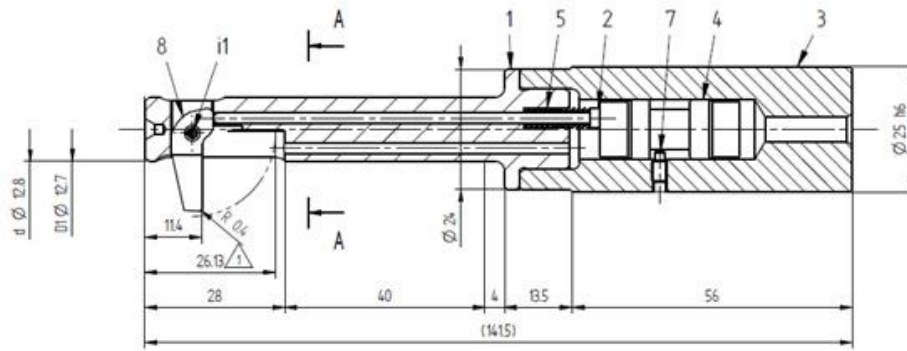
Розточна головка зі зворотнім ходом
